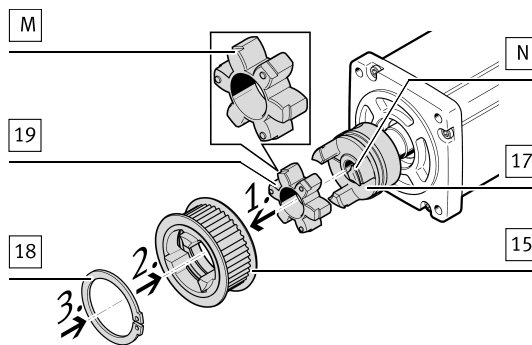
Крепление шкива зубчатого ремня на стороне мотора
